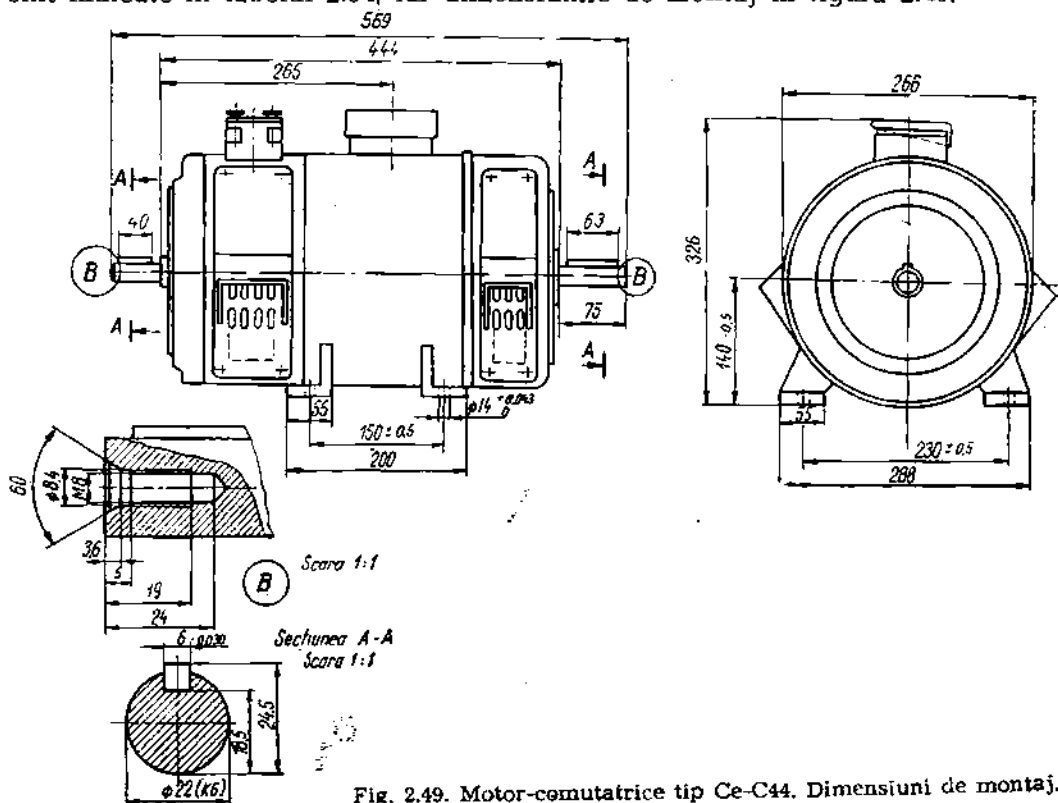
Motor-comutatrice tip Ce-C44. Dimensiuni de montaj.
